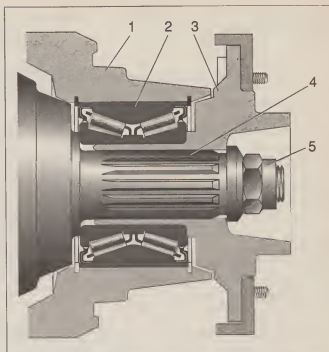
Узел колеса: 1 – поворотный кулак; 2 – подшипник; 3 – ступица; 4 – вал (ось); 5 – гайка.
